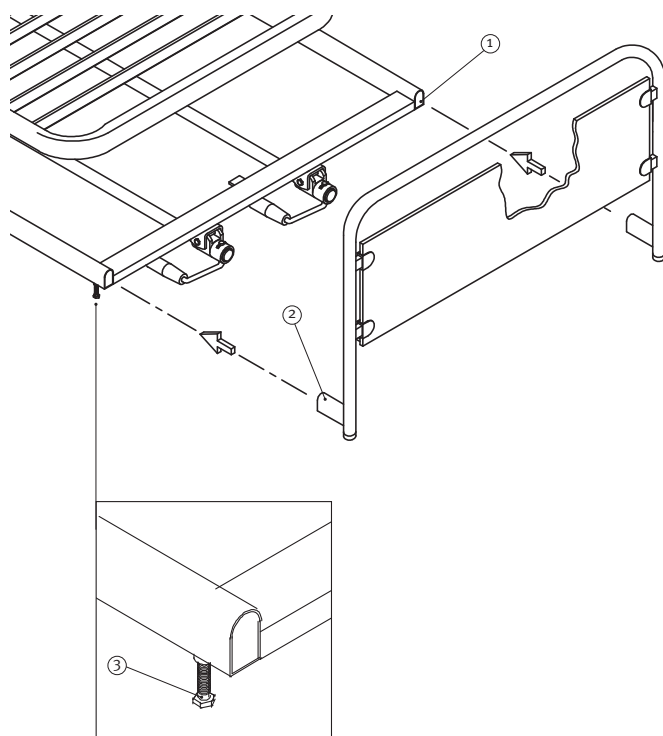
Montaggio delle spalle pediera/testiera.
